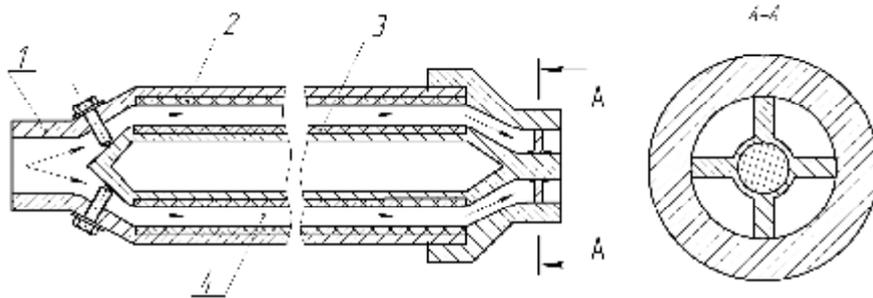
Схема триботрубки устройства для повышения сцепления колеса с рельсом
